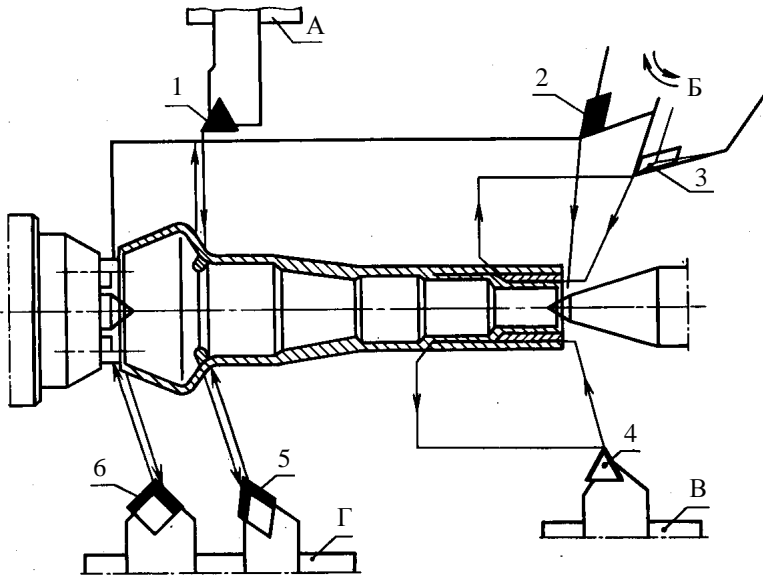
Схема обточування на токарно-гідрокопіювальному напівавтоматі АЛ:
